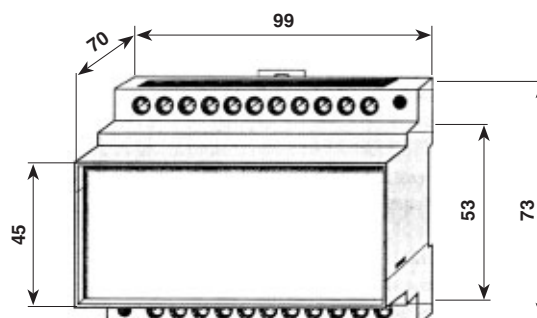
Габаритные размеры АСТРО-ИЗО-470
